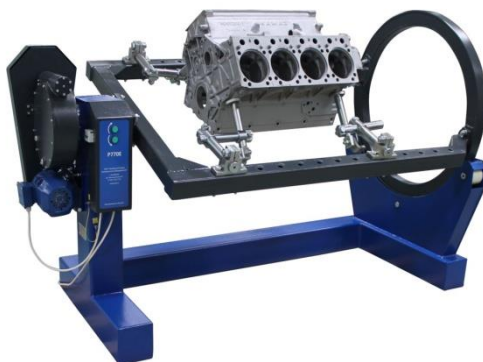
Универсальный стенд для разборки-сборки различных узлов и агрегатов
